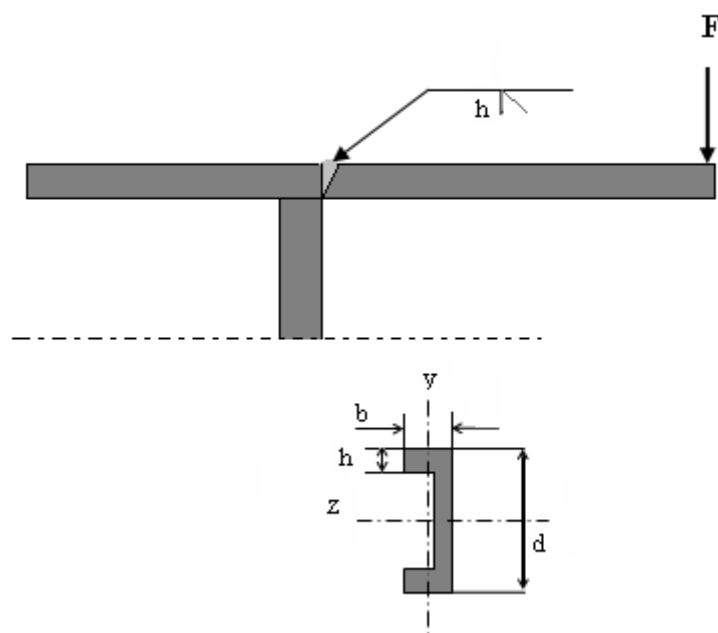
Diagrama de soldadura entre columnas
